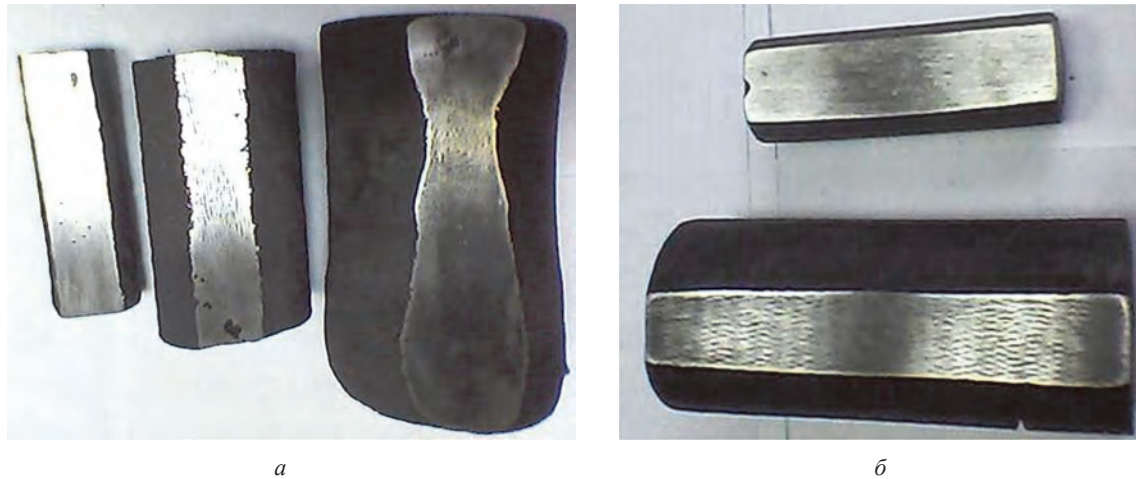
Общий вид образцов отливок (а) диаметром 33, 63 и 83 мм и поковок (б) диаметром 33 и 63 мм, подвергавшихся исследованию для стали 4X5MФ1С
